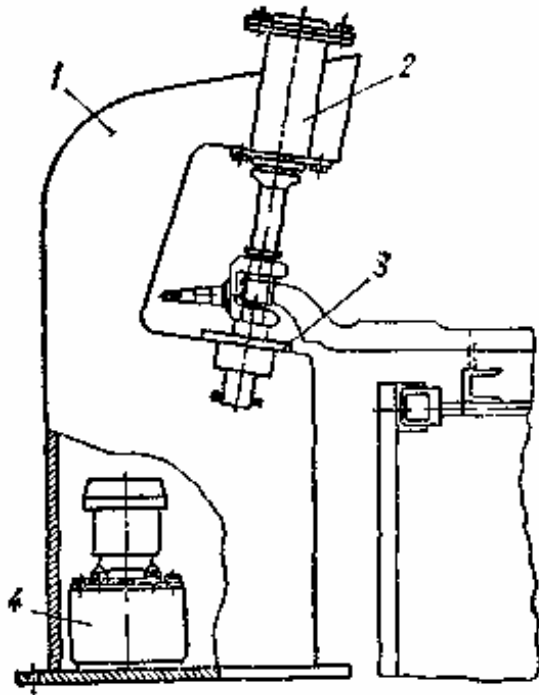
Специальный гидравлический пресс для выпрессовывания шкворней:
